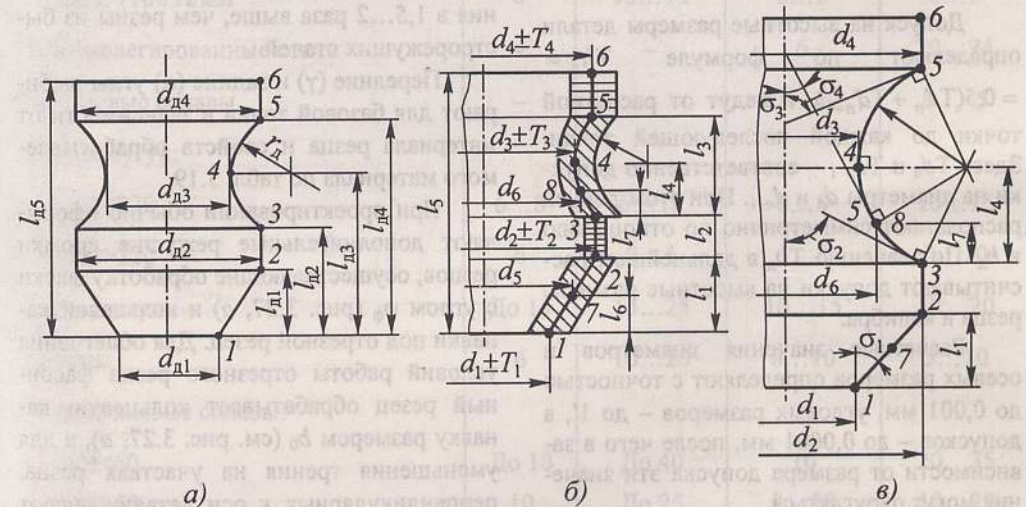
Чертеж детали (а), схема полей допусков (б) и углы профиля в разных точках детали (в)
